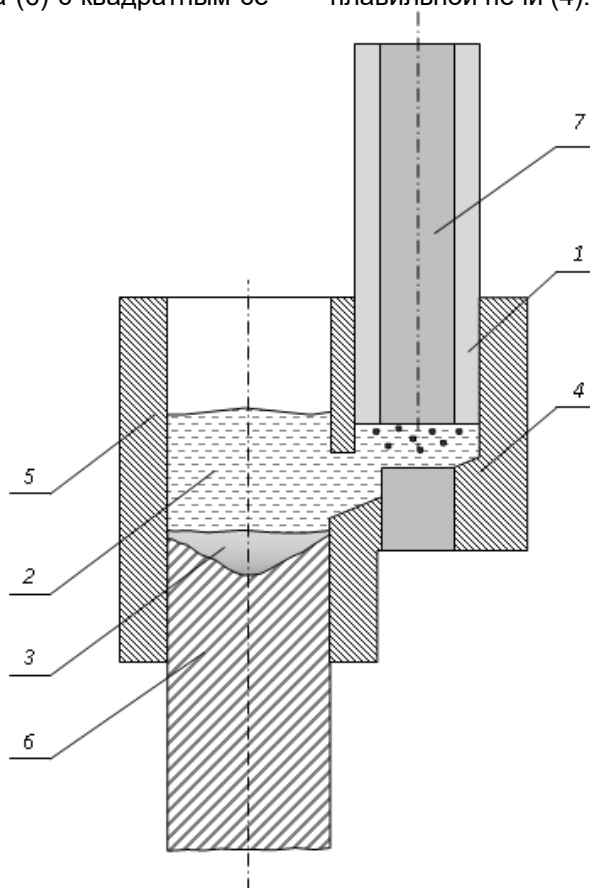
Схема установки: 1 – мундштук; 2 – жидкий шлак; 3 – жидкий металл; 4 – плавильная печь; 5 – литейная форма; 6 – отливка; 7 – расходуемый электрод
